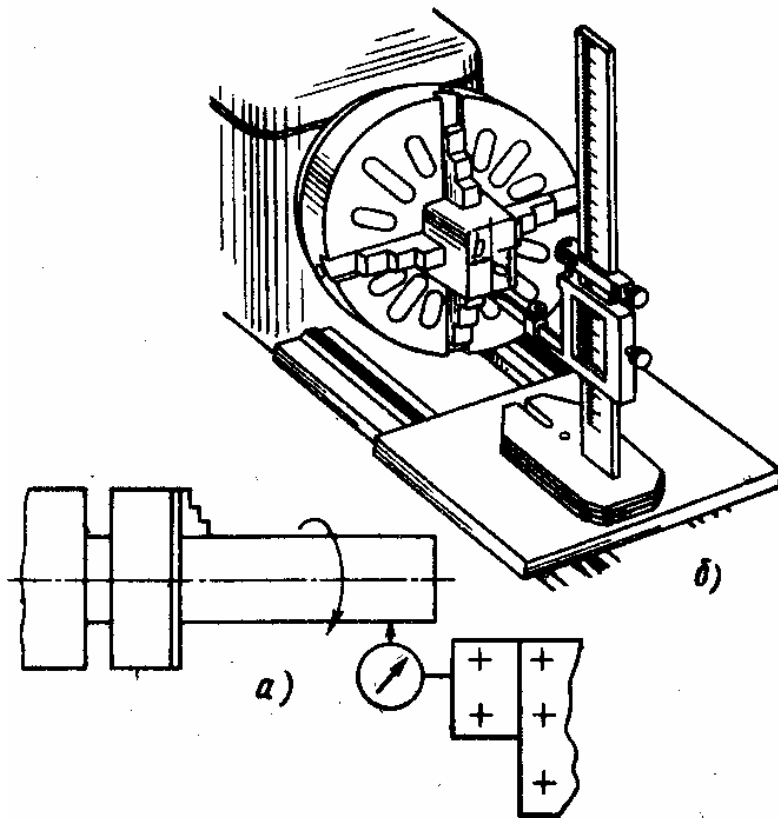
Схеми установлення заготовок в патронах з вивіренням
